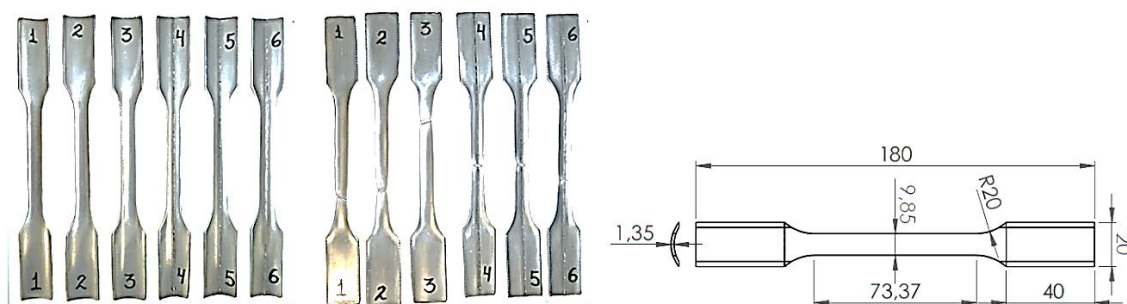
Amostras antes e pós-ensaio (esquerda), desenho CAD com dimensões em milímetros (direita).
